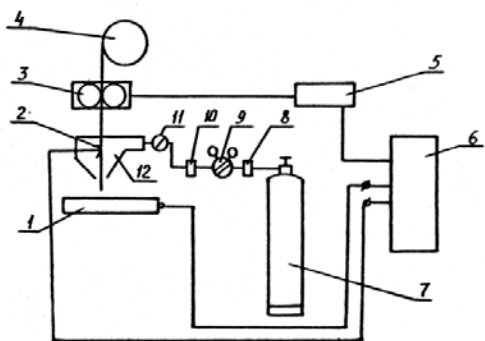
Схема устройства поста для сварки (наплавки) в среде углекислого газа и смесях защитных газов:
